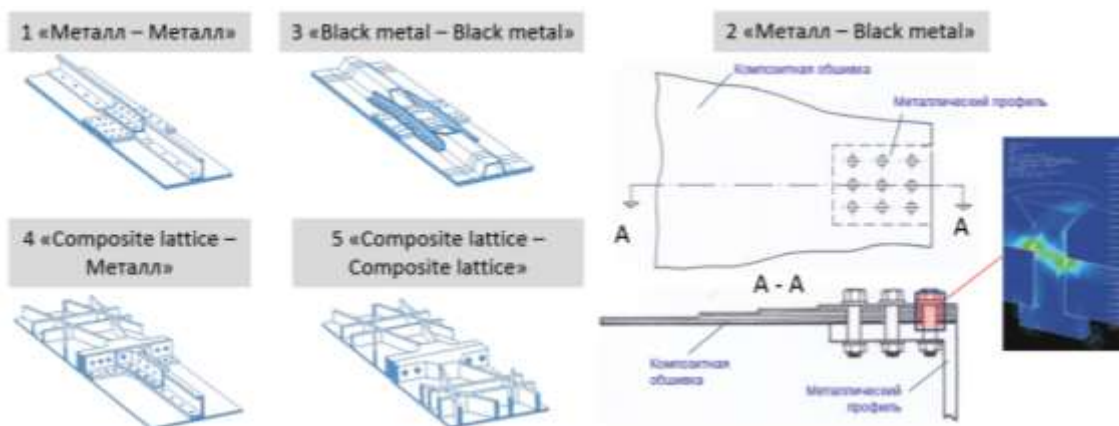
Типы болтовых соединений композитных и металлических конструкций
